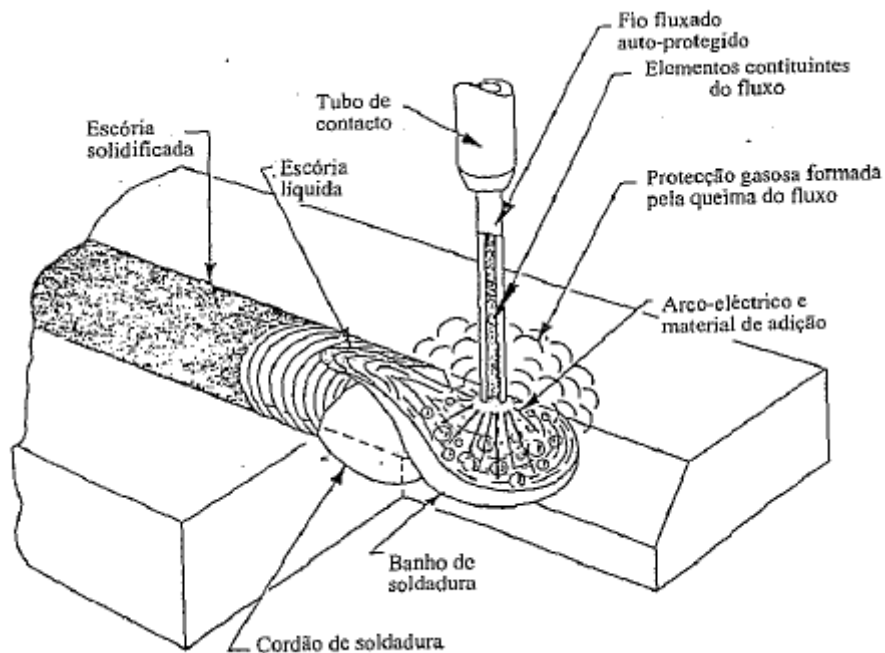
Ilustração do processo de soldadura FCAW (auto protegido) [16].
